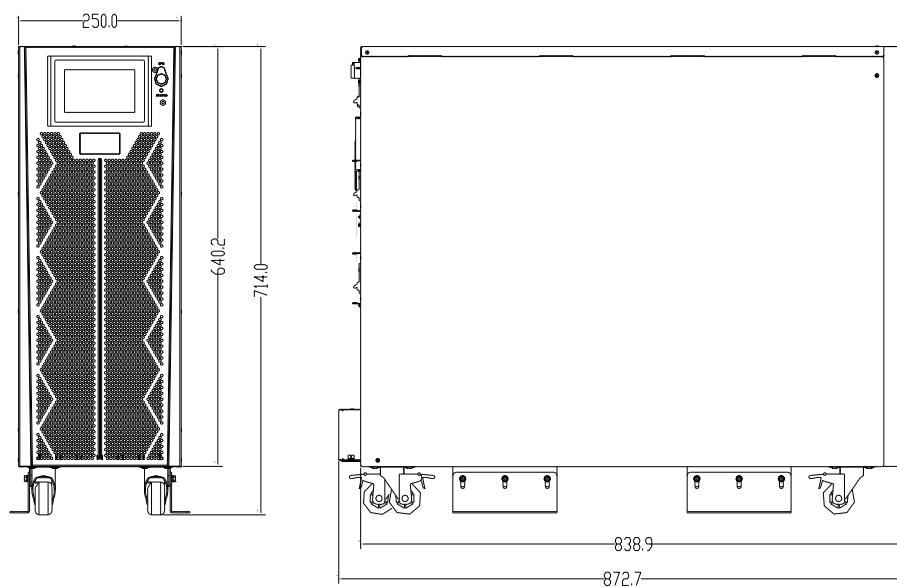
Размеры ИБП 10/15 kVA (увеличенный типоразмер)
